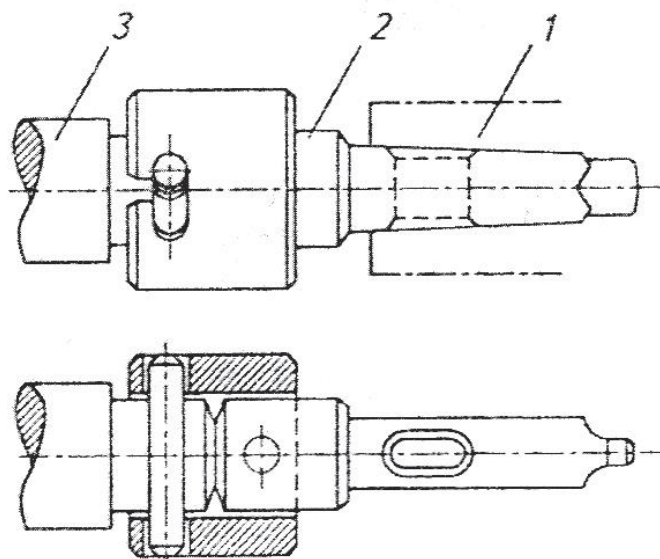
Схема соединения шпинделя станка с борштангой:
